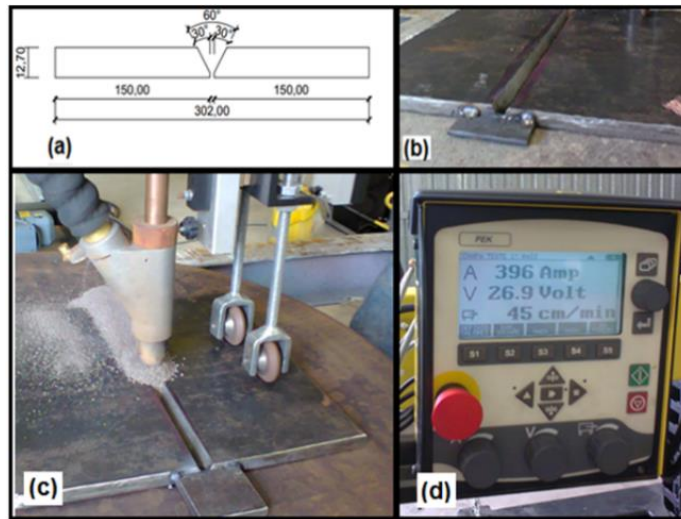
Junta soldada: (a) Croqui do chanfro da junta; (b) Junta de Topo 300 x 300; (medidas em mm); (c) Junta recebendo soldagem via arco submerso; (d) Parâmetros utilizados para efetuar as soldas.
